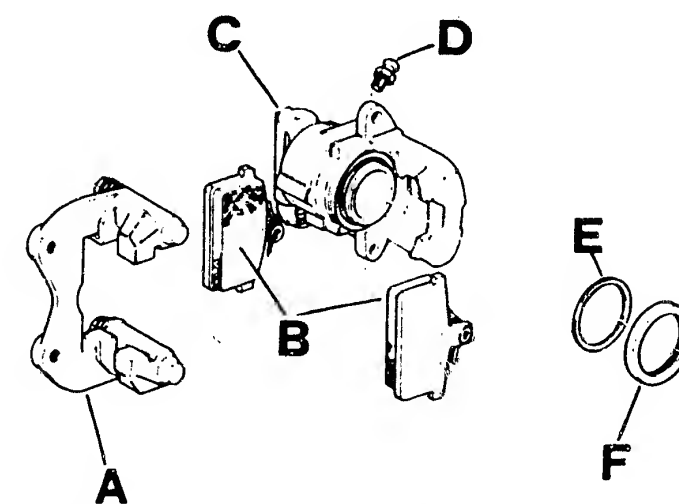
Einzelteile des hinteren Bremssattels: A Bremsträger – B Bremsklötze – C Bremssattel – D Entlüfterschraube – E Dichtring – F Schutzmanschette.
